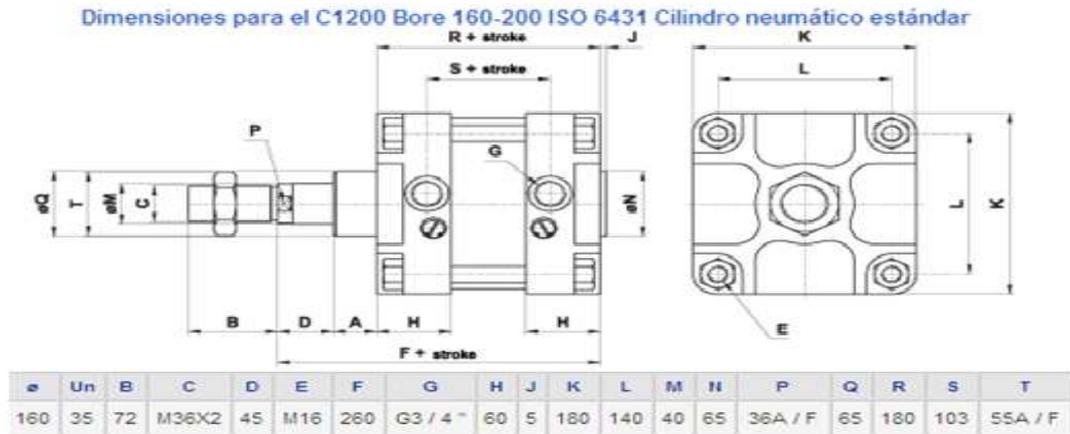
Dimensiones Pistón neumático para movimiento cuchilla suministro de producto
